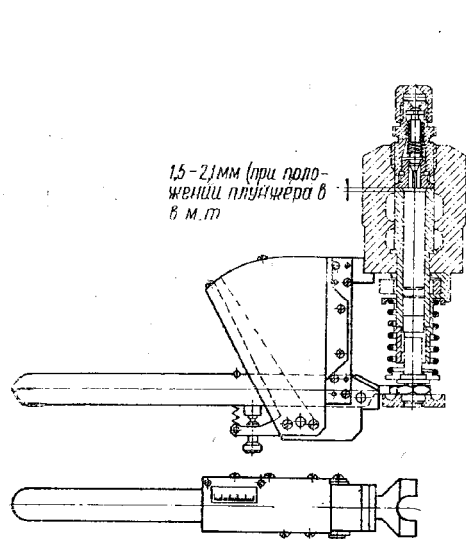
Приспособление ЛМ 9579-245 для проверки зазора между верхним торцом плунжера и седлом нагнетательного клапана
